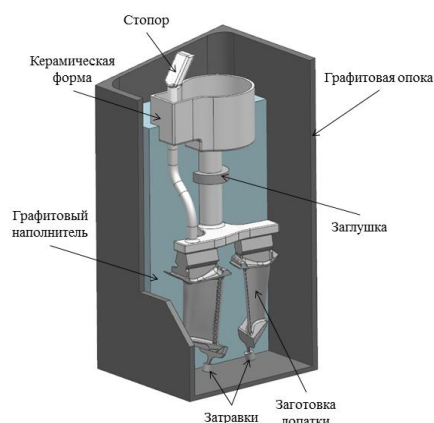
3D-модель отливки лопатки турбины и литейного блока
